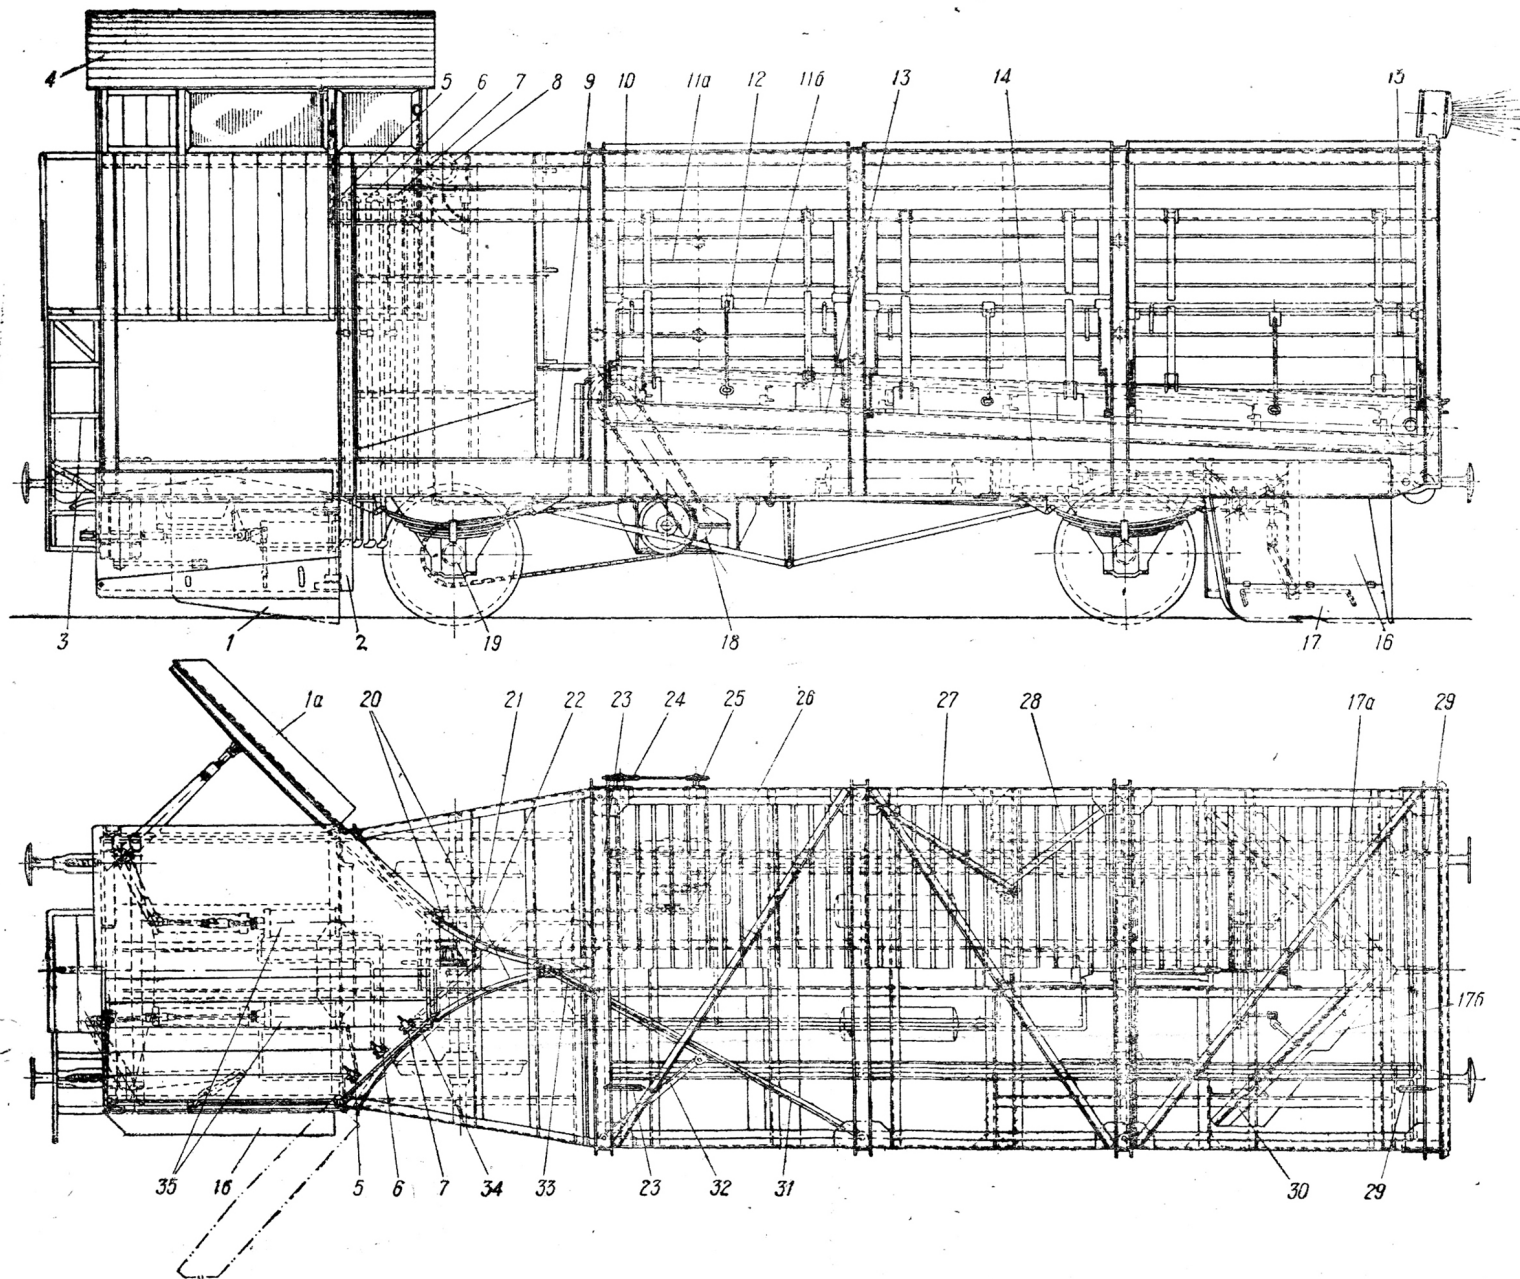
Шестой полувагон-снегоочиститель. Общий вид
